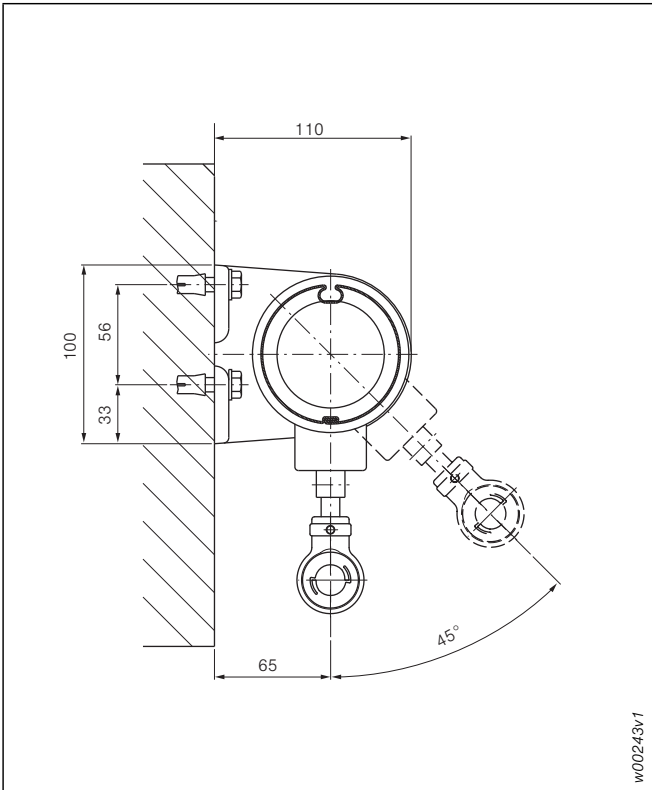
Wandmontage mit außenliegendem Kurbelantrieb
